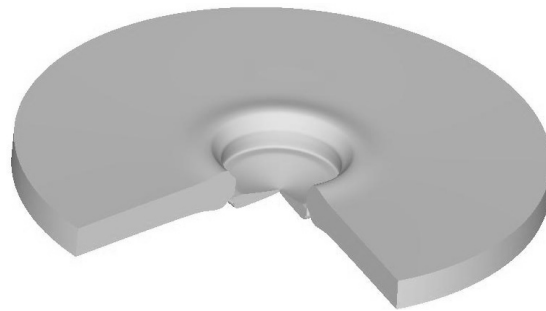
Заготовка в розрізі на завершній стадії пробивання перемички
